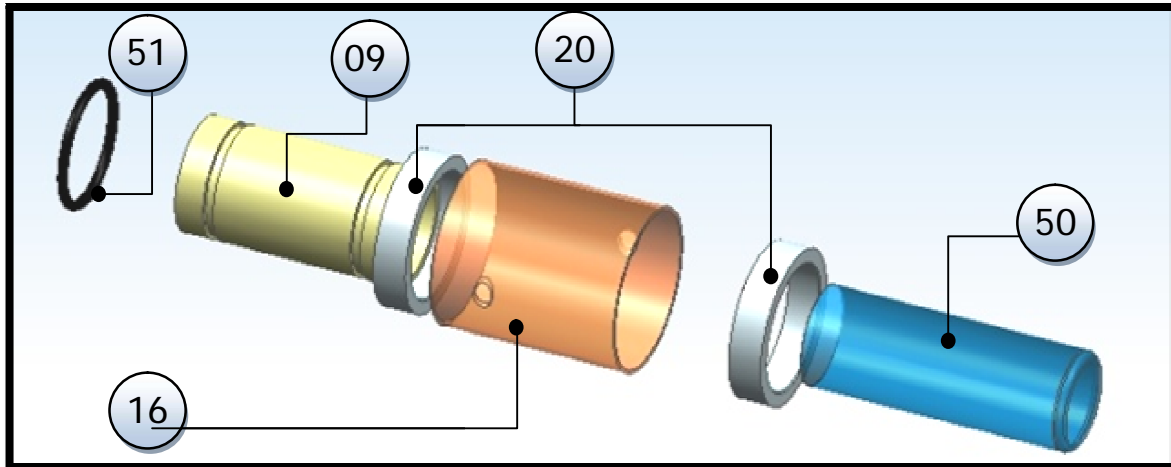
Vista explosionada del cilindro. Imagen obtenida del modelo realizado en software CAD/CAM del motor Stirling Silver II. Fuente: elaboración propia.
